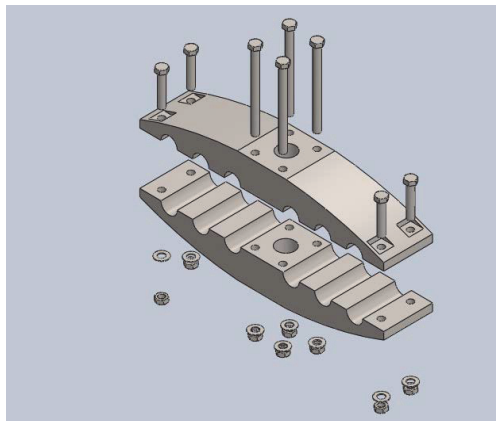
Vista explosionada del nuevo diseño del herraje
